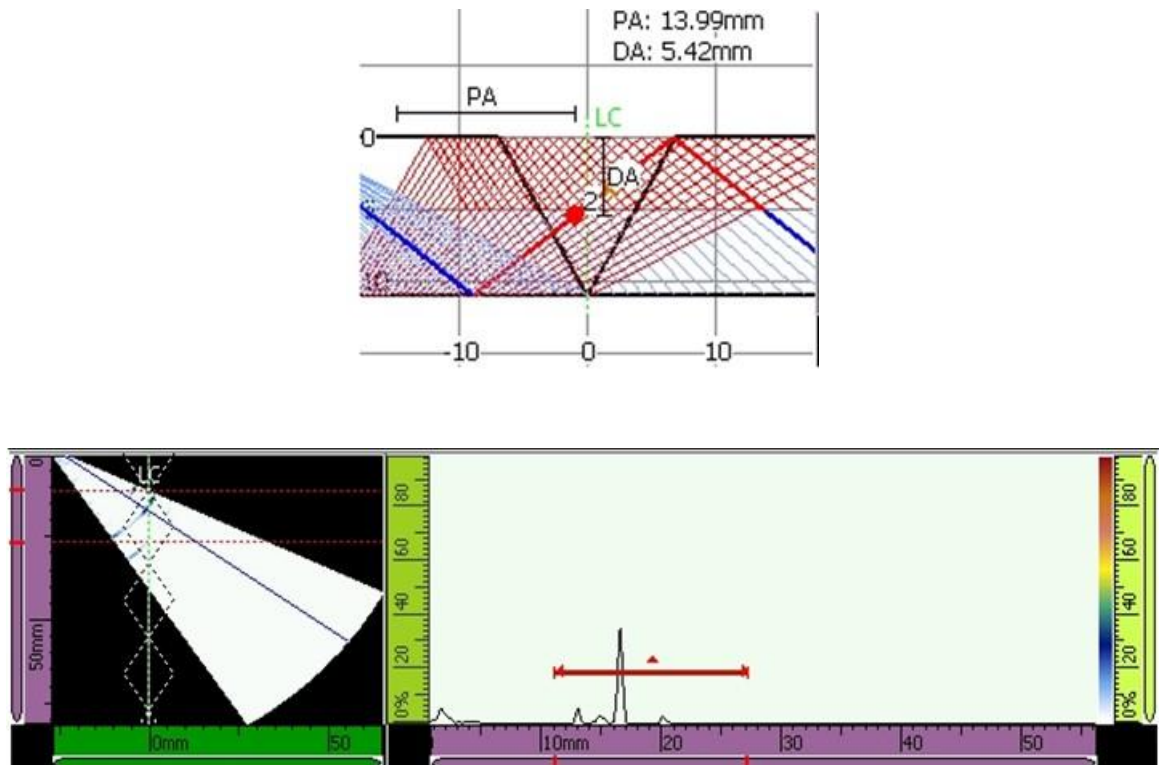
Tubería de inspección de soldadura punto 2.
